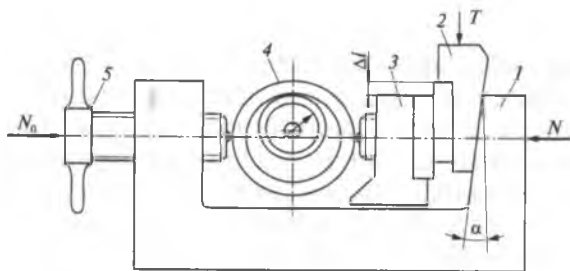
Схема процесса холодной сварки сдвигом
